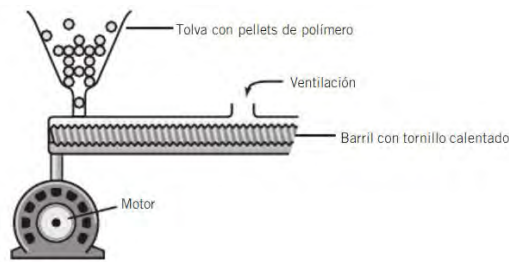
Esquema de extrusión de pellet por medio de tornillo sin fin.
